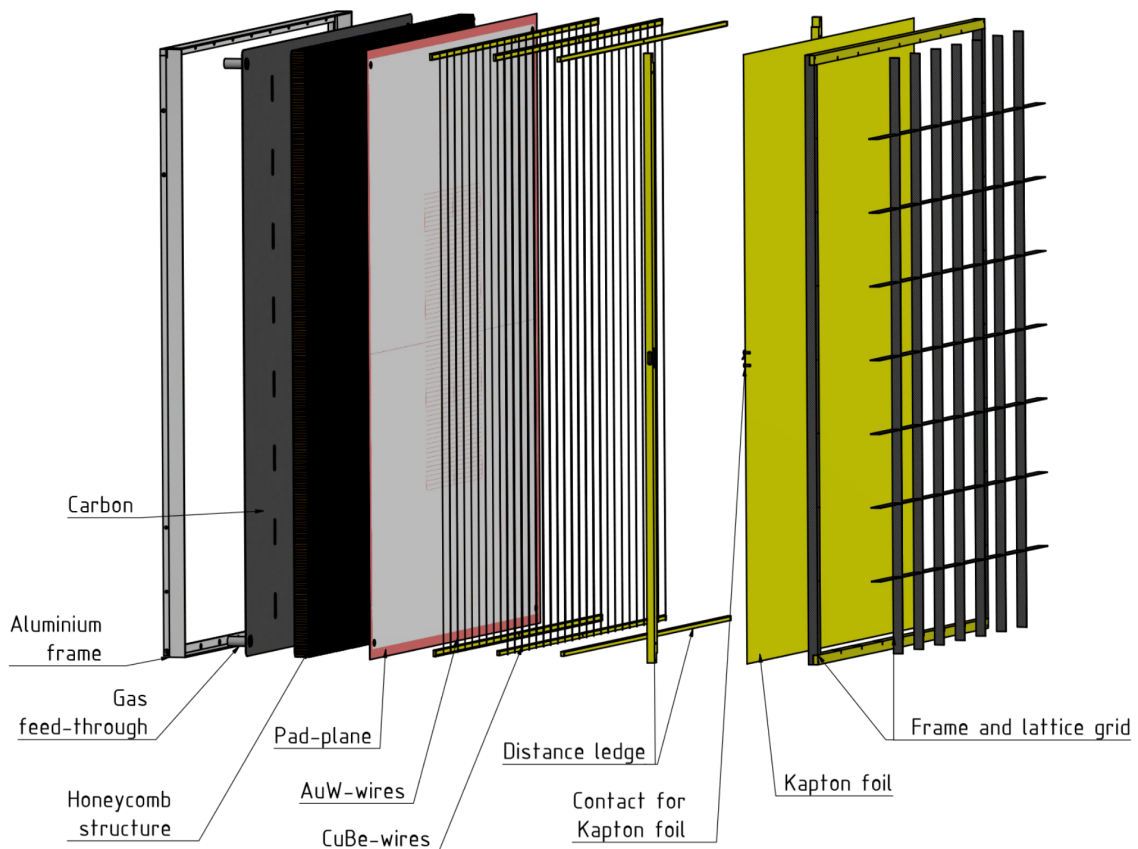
Die verschiedenen Ebenen einer CBM-TRD-Kammer sind in einer Explosionsansicht dargestellt [Col18].
